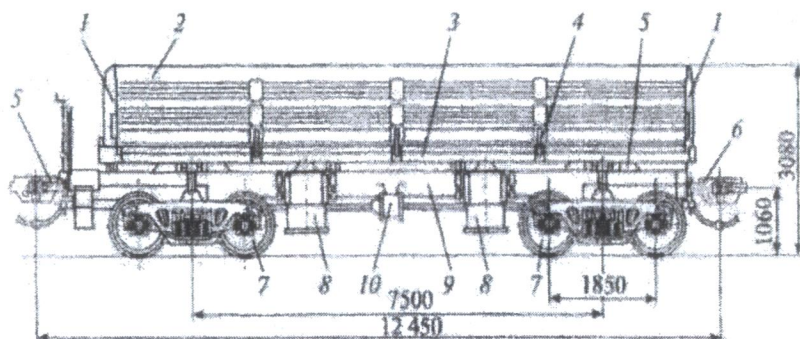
Вагон-самосвал (думпкар) модели 31-674: 1 - лобовая стенка с шарнирно-рычажным механизмом открывания борта; 2 - продольный борт; 3 - верхняя рама; 4 - петля; 5 - упор; 6 – автосцепка СА-3; 7 - ходовая тележка 18-100; 8 - пневмоцилиндр наклона кузова; 9 - нижняя рама; 10 - тормозная система
